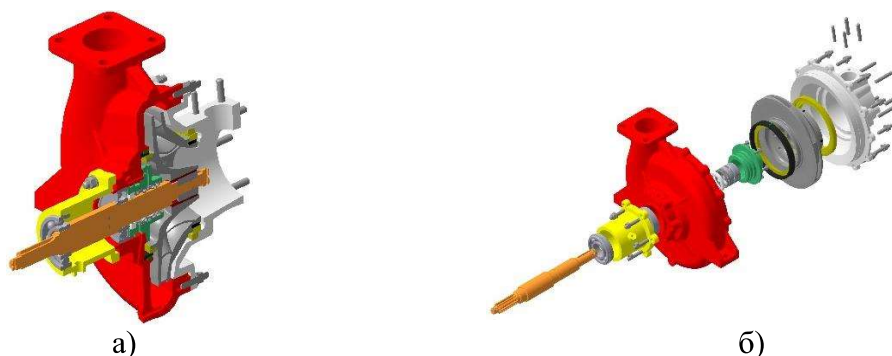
Пожежний насос: а – розріз, б – рознесений вид
